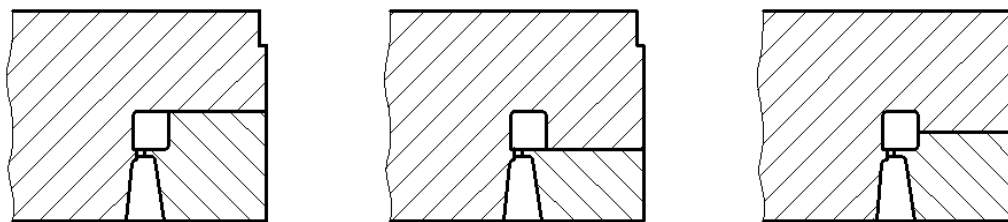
Варианты размещения сварочной камеры:
